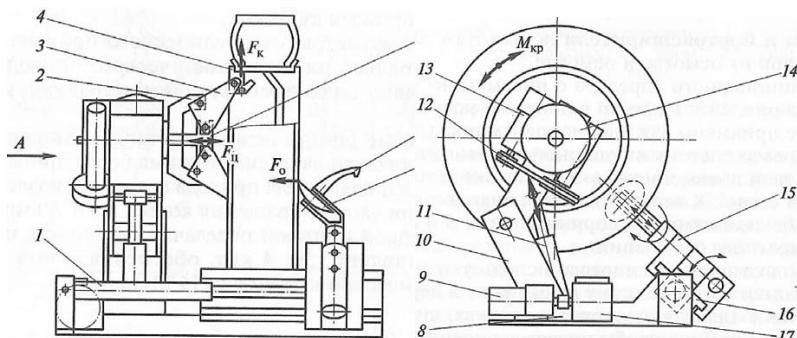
Устройство стенда для монтажа и демонтажа шин колес грузовых автомобилей (стрелками на виде А показаны направления движения монтажной стойки и монтажной консоли): 1 – гидроцилиндр привода монтажной консоли; 2 – корпус зажимного механизма; 3 – рычаг; 4 – кулачок; 5 – шток гидроцилиндра привода зажимного механизма; 6 – монтажная головка; 7 – отжимной ролик; 8 – основание; 9 – электродвигатель привода насоса; 10 – стойка; 11 – гидроцилиндр подъема стойки; 12 – ременная передача; 13 – электродвигатель привода вращения колеса; 14 – червячный редуктор; 15 – монтажная консоль; 16 – направляющая; 17 – насос гидравлической системы стенда; M_{kp} – крутящий момент, приложенный к колесу; F_u – сила на штоке гидроцилиндра привода зажимного механизма; F_K – сила прижатия кулачков к закраине диска; F_o – отрывная сила на отжимной лопатке
